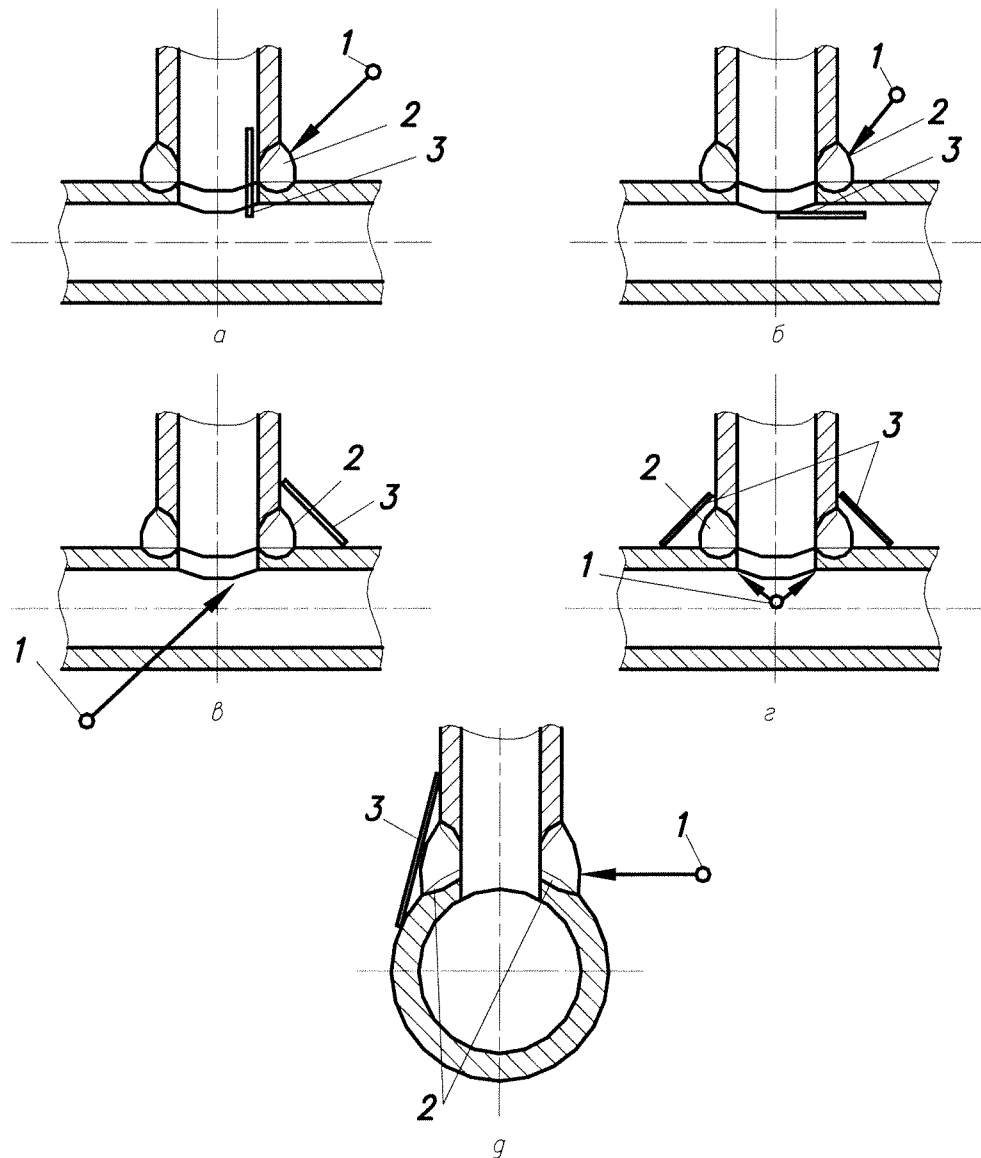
Схемы контроля сварных соединений вварки штуцеров. Обозначения см. рис. 5.2
